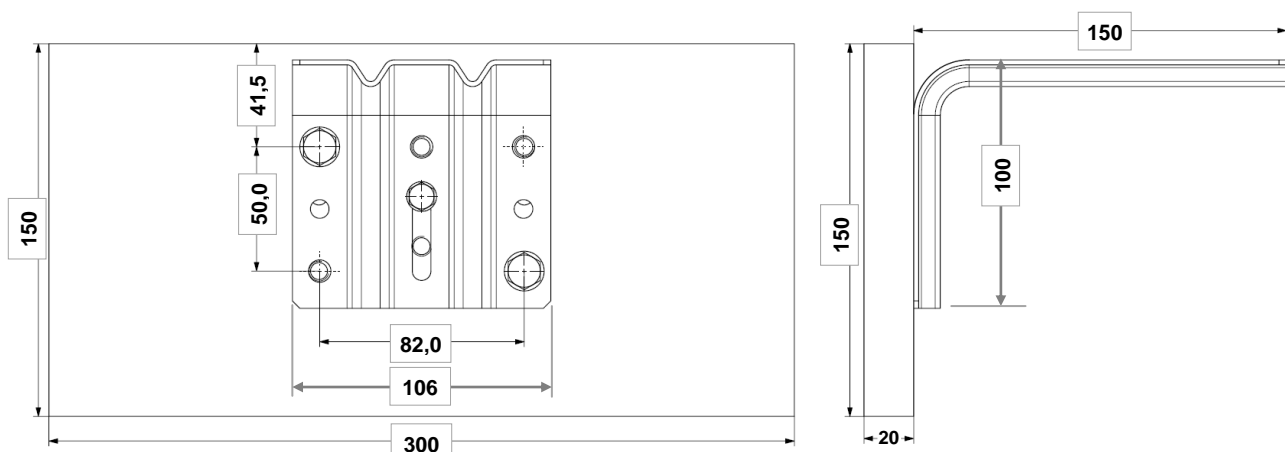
geprüfter Montagewinkel mit Aufspannplatte
